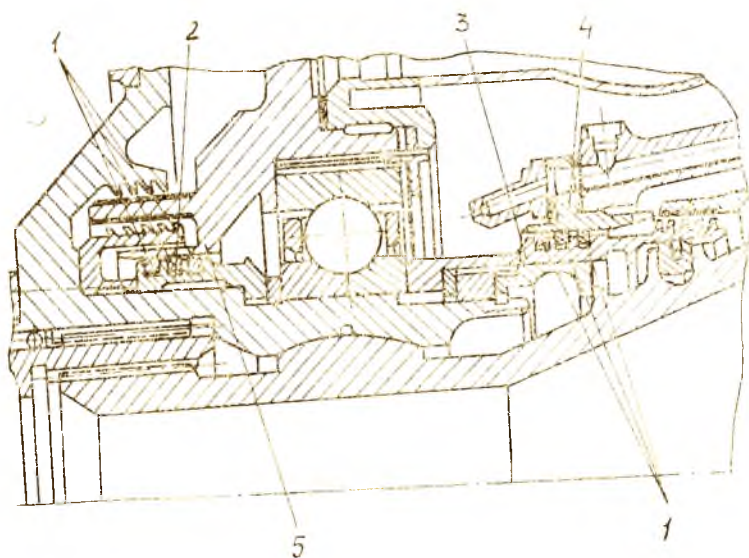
Уплотнения контактными кольцами опоры компрессора вертолетного ГТД
